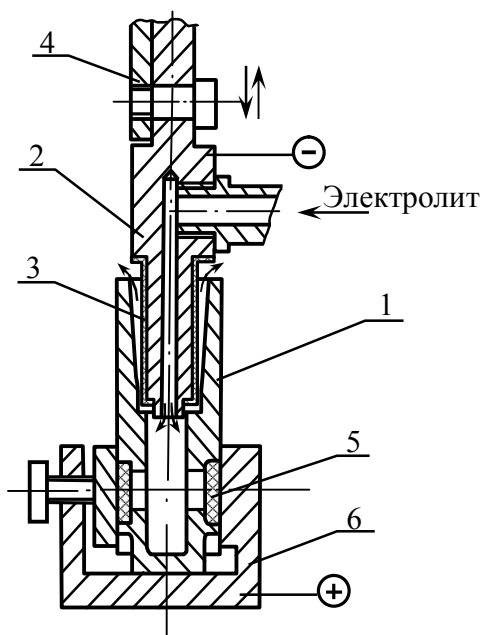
Схема скругления острых кромок паза детали «Корпус»:
